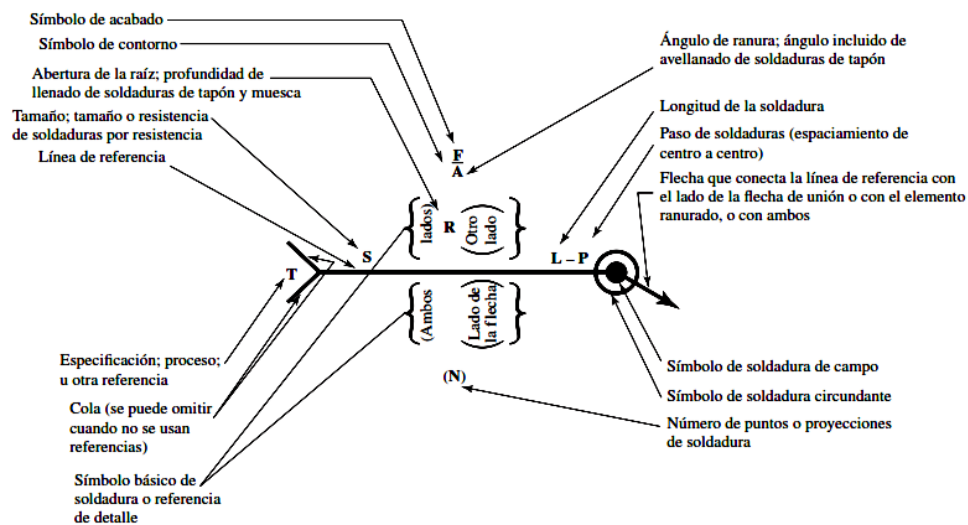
Representación simbólica de soldadura estándar AWS [22].
